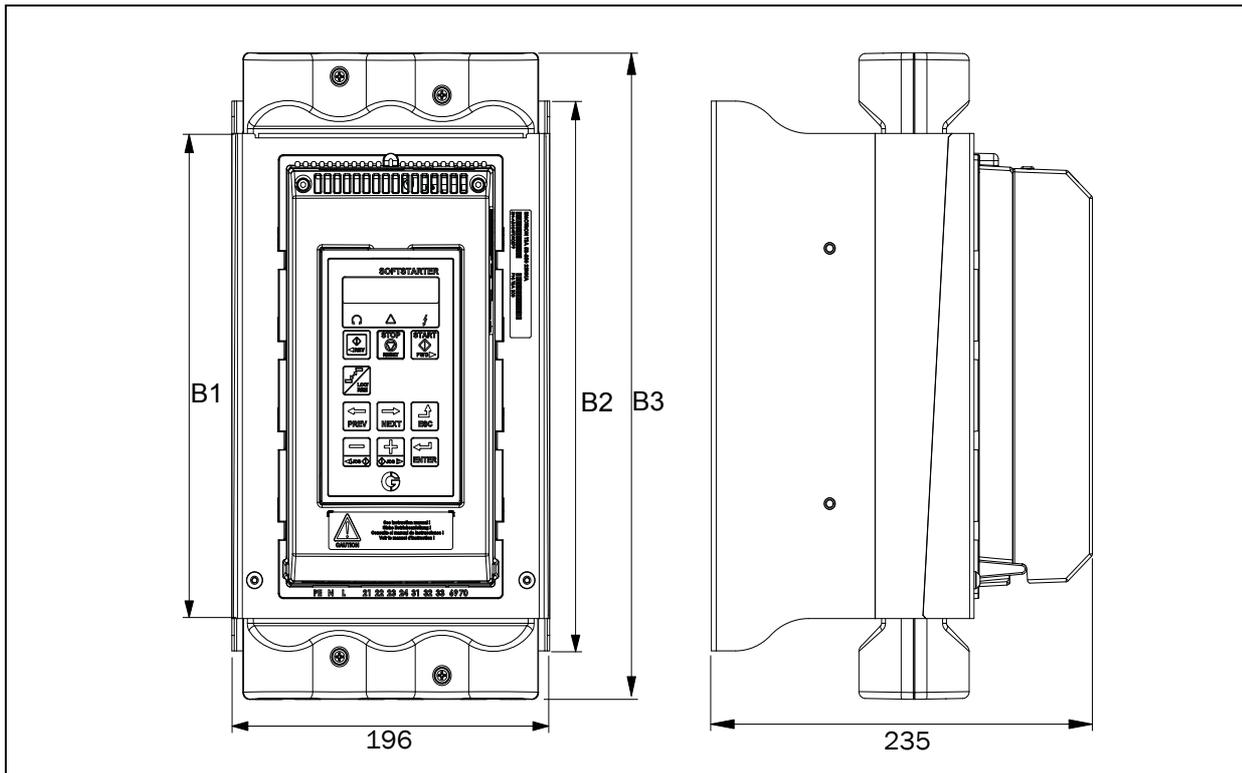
Габаритные размеры Emotron TSA типоразмера 3.
